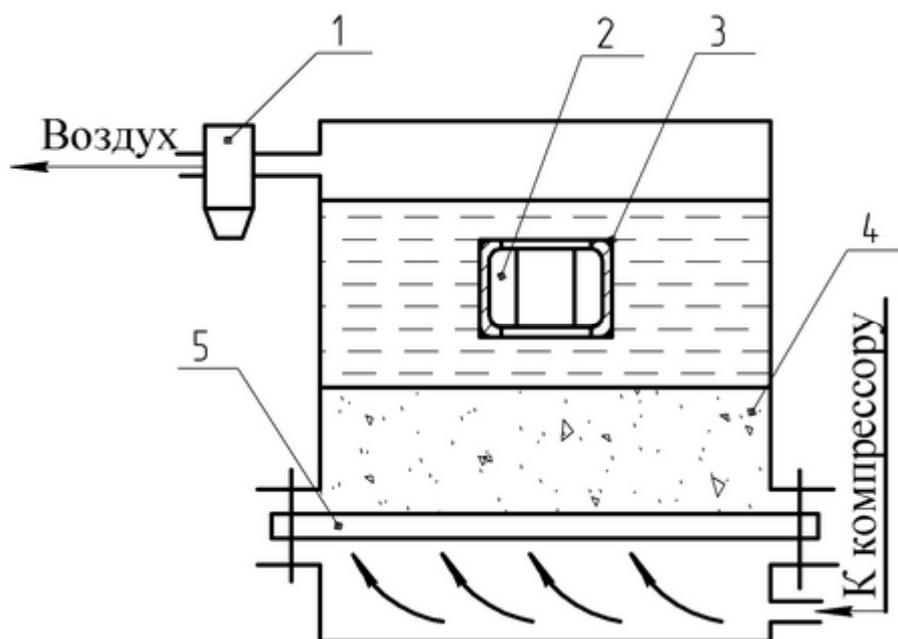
Схема установки для вихревого напыления пластмассовых покрытий: 1 – уловитель порошка; 2 – напыляемая деталь; 3 – изоляция; 4 – камера; 5 – пористая перегородка
